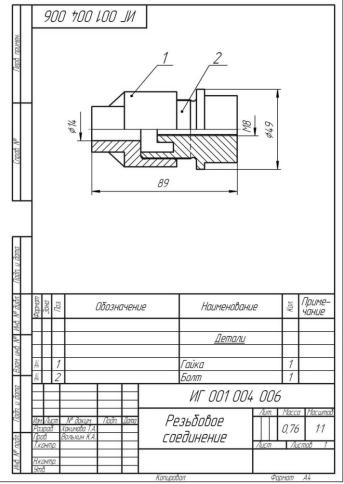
Ассоциативный чертеж резьбового соединения.
